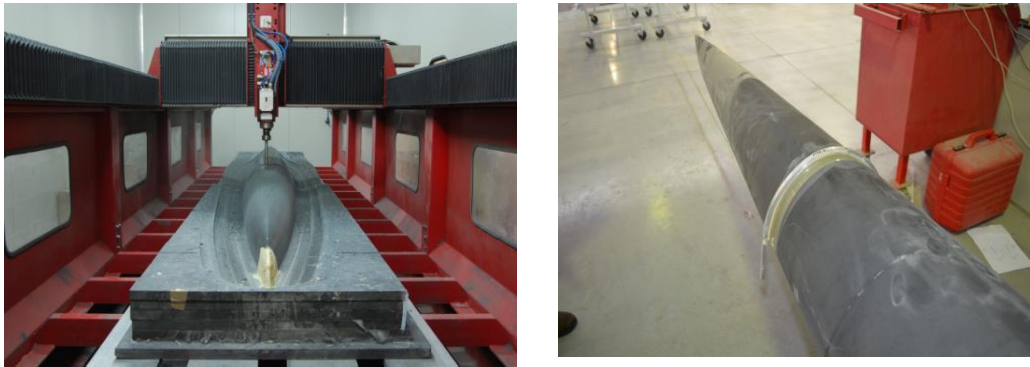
Maquinagem de um protótipo (esq.) e verificação dimensional (dta.).
